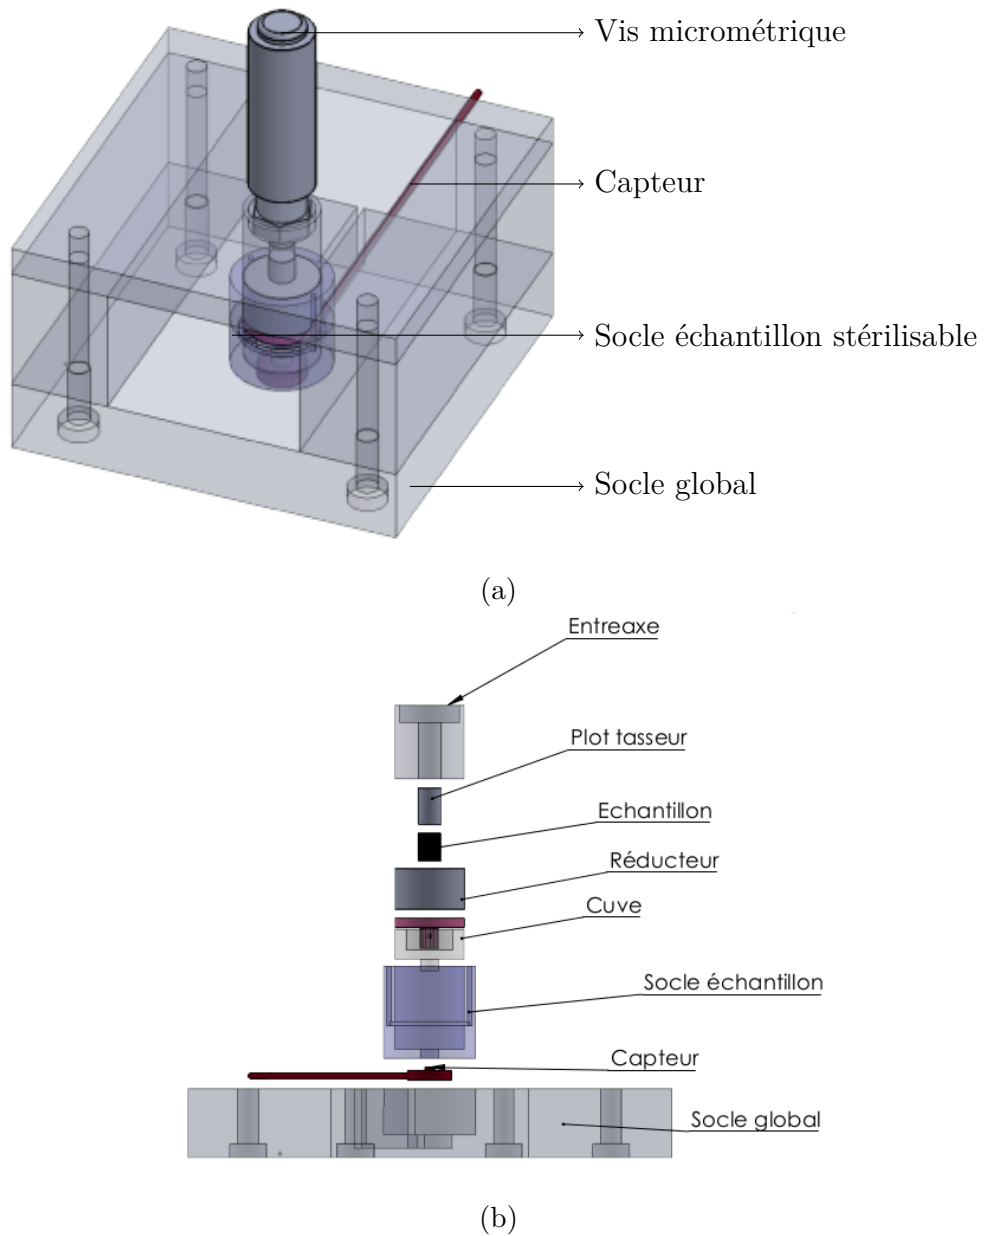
(a) Vue globale et (b) vue éclatée de la machine de compactage.
